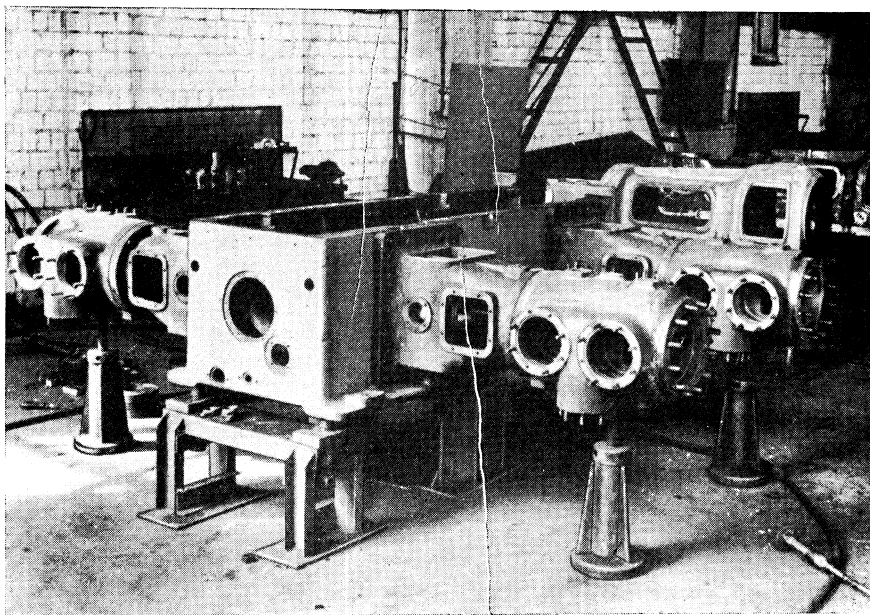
Аммиачный компрессор АО-1200 со встречным движением поршней. Сборка опытного образца.
